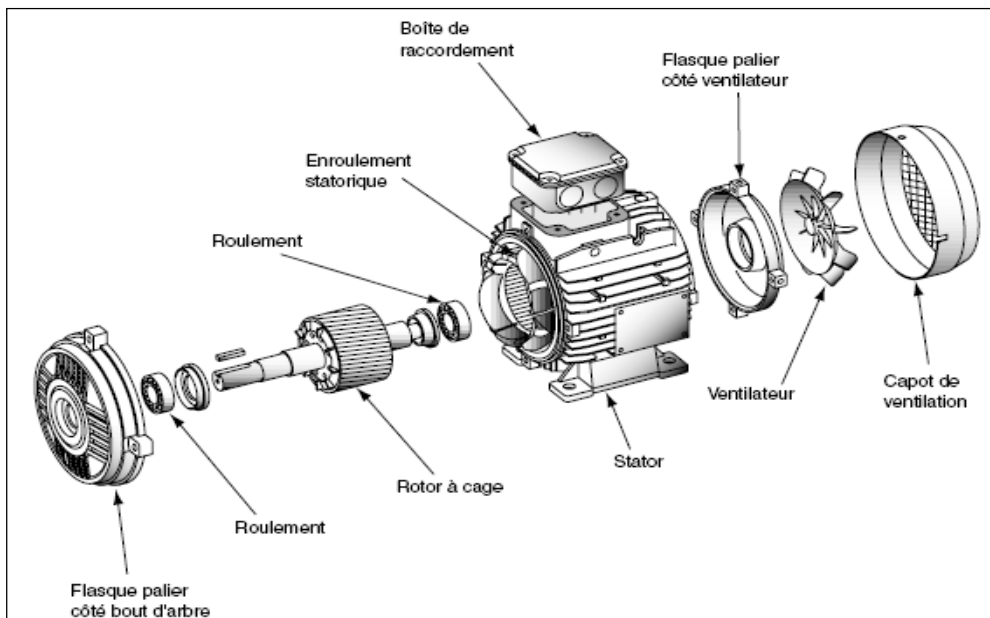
Vue éclatée d'un moteur à induction à cage d'écureuil
